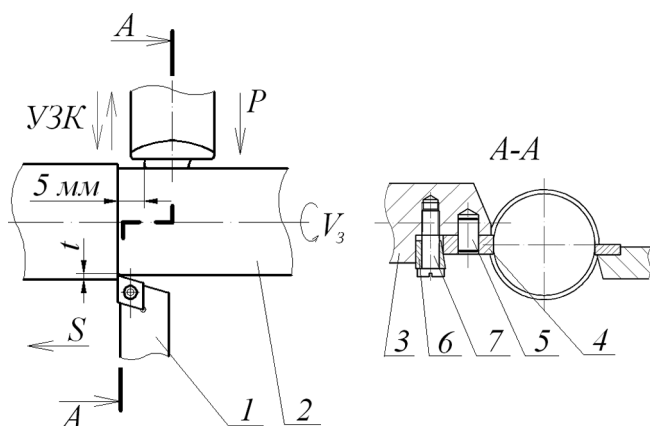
Схема установки для комбинированной обработки точением и УЗТВ: 1 — резец; 2 — заготовка; 3 — концентратор; 4 — твердосплавный выглаживатель; 5 — штифт; 6 — клин; 7 — винт
